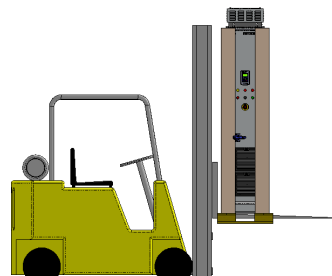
Vista trasera de carretilla elevadora bajada
